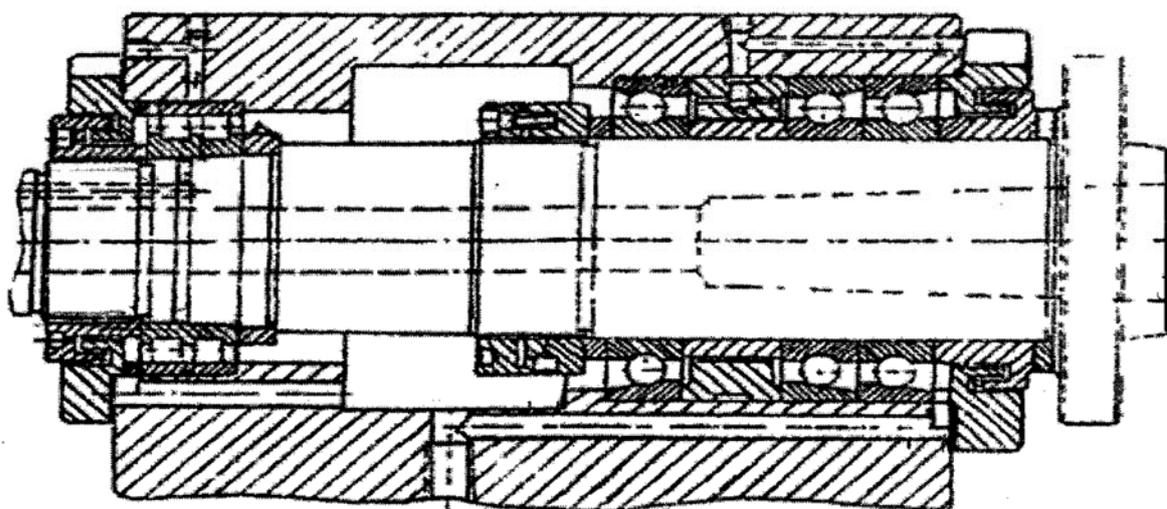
Шпиндельный узел станка на роликоподшипниках типа 3182100 в задней опоре и на подшипниках типа 36000 и 46000, собранных в комплекте по три по схеме дуплекс 0-образной в передней опоре
